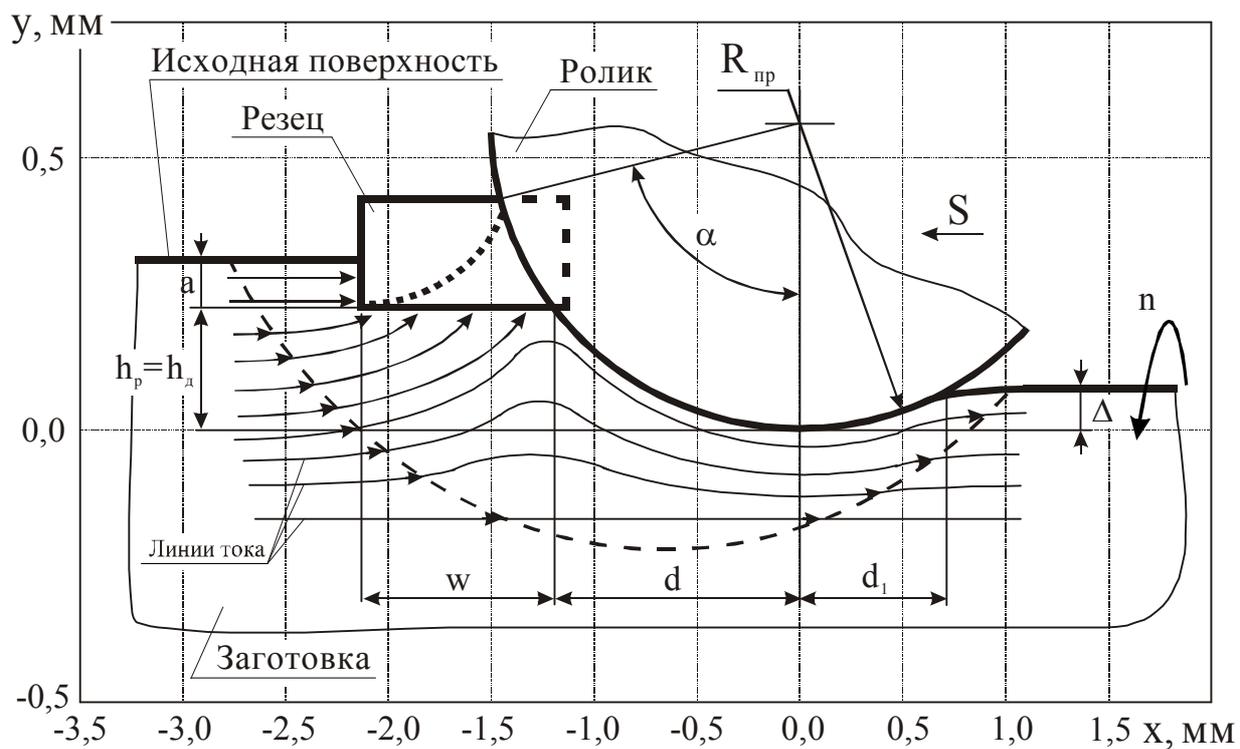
2-я схема размерного совмещенного обкатывания
